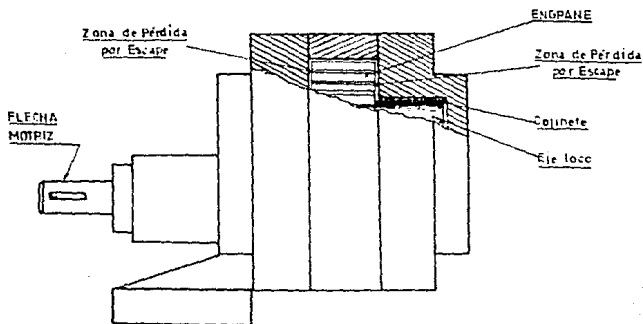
Vista en corte de una bomba de engranes de baja presión
